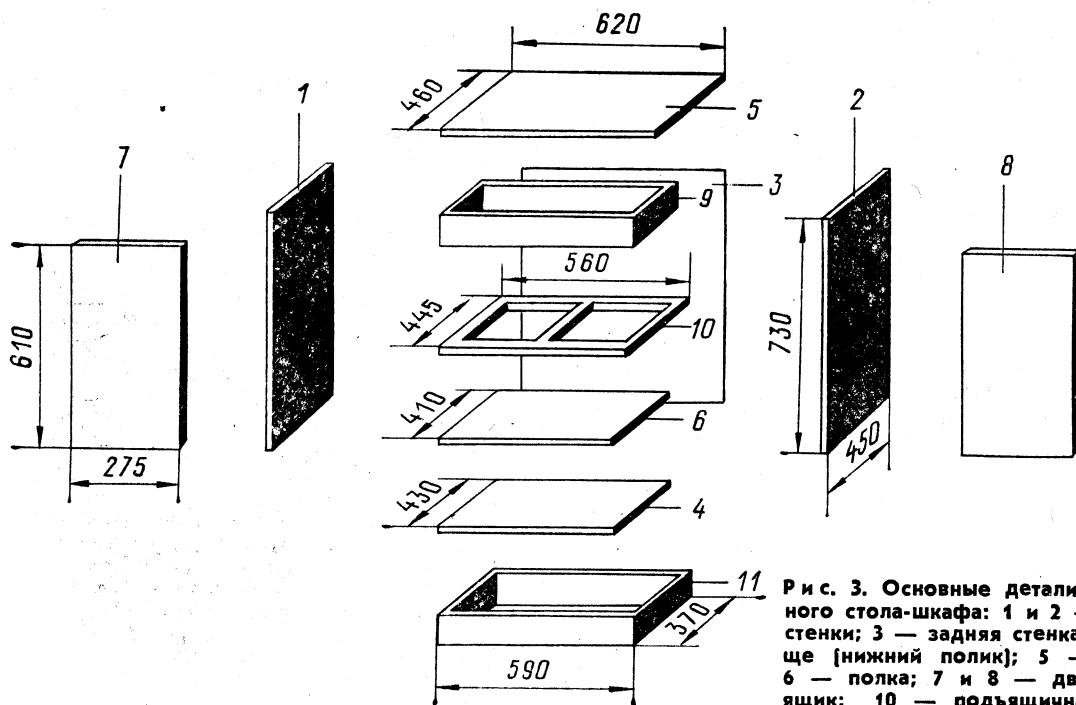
Основные детали разделочного стола-шкафа: 1 и 2 — боковые стенки; 3 — задняя стенка; 4 — днище (нижний полик); 5 — крышка; 6 — полка; 7 и 8 — дверки; 9 — ящик; 10 — подъяничная рамка; 11 — цоколь
